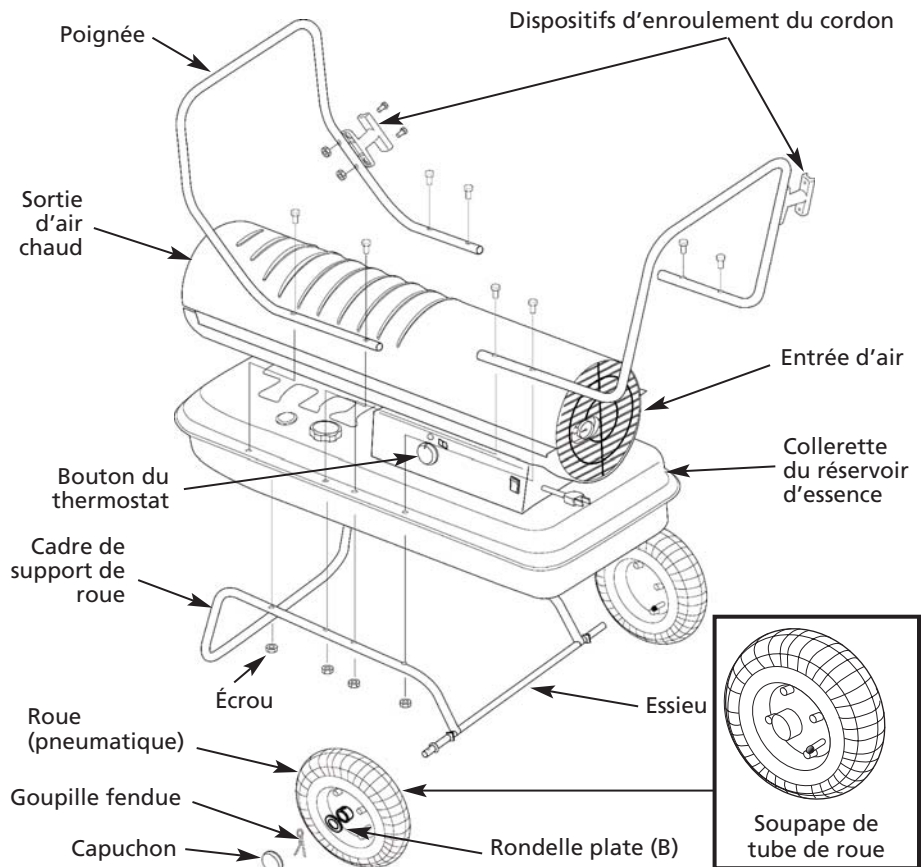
Assemblage des modèles 3VE50B, 3VE51B et 3VE52B
